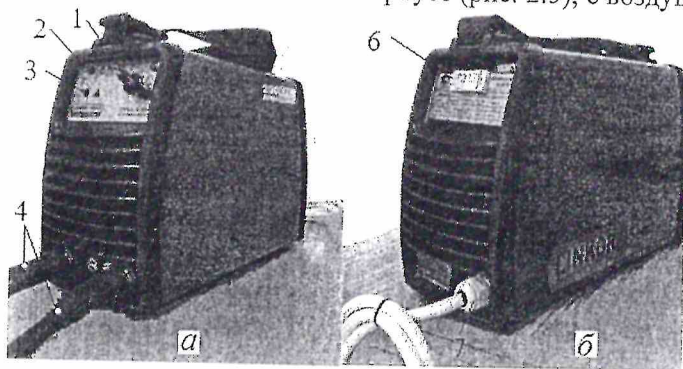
Внешний вид инверторного сварочного аппарата:
